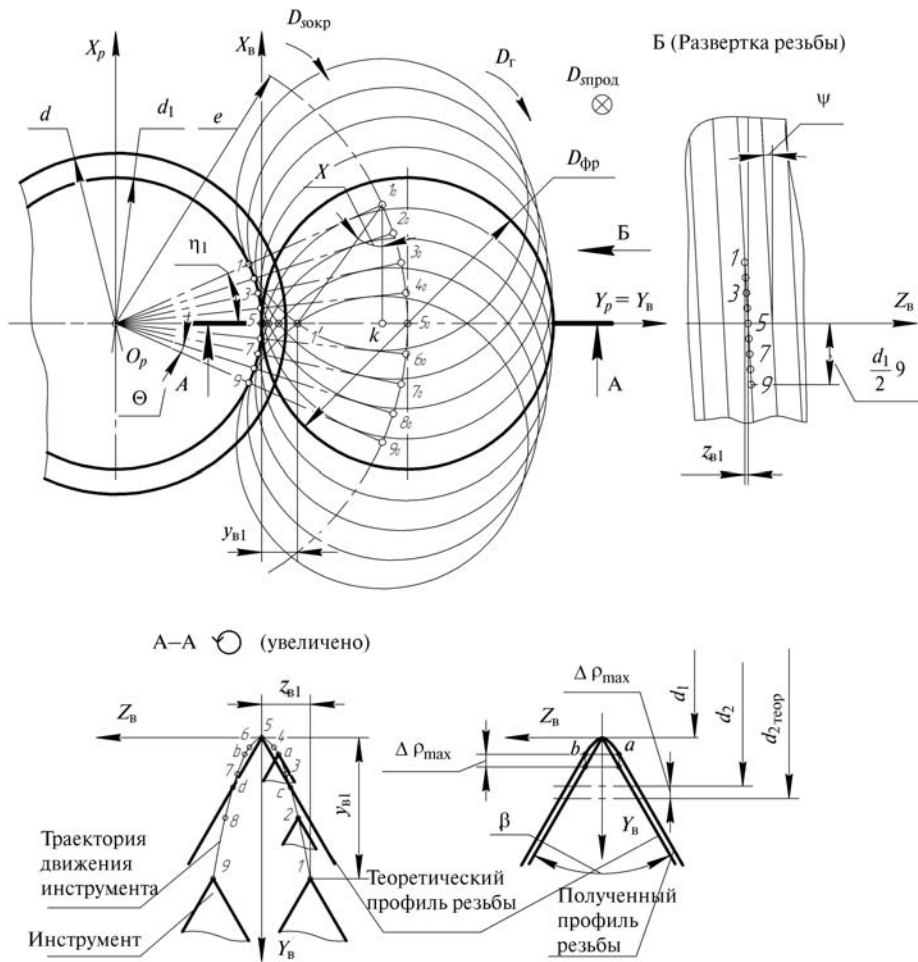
Схема формирования профиля наружной резьбы резьбовой фрезой внешнего касания:
